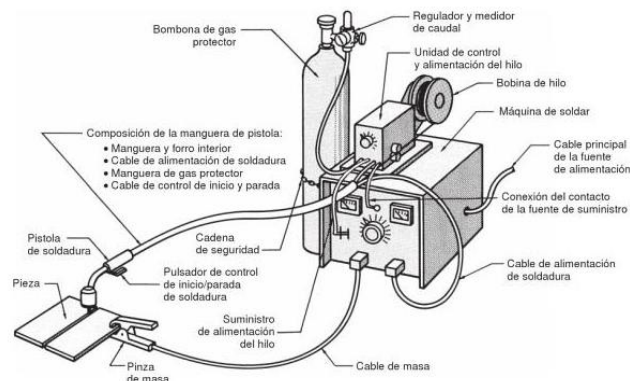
Equipo de soldadura por arco metálico con gas protector. Fuente: Jeffus, 2008
